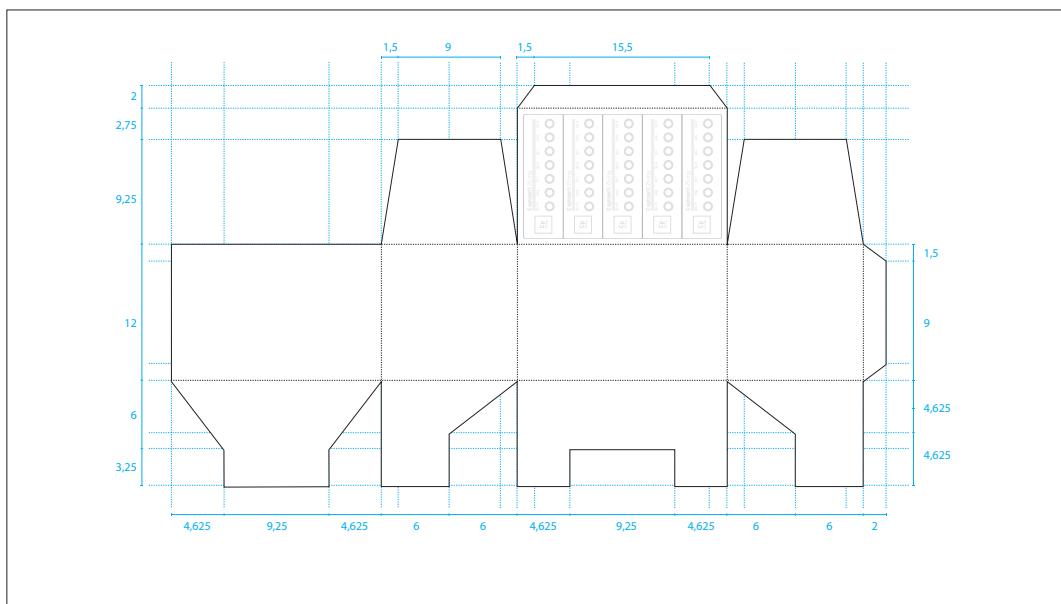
Planimetria da caixa de fornecimento do blister menor (Padrão 1).
